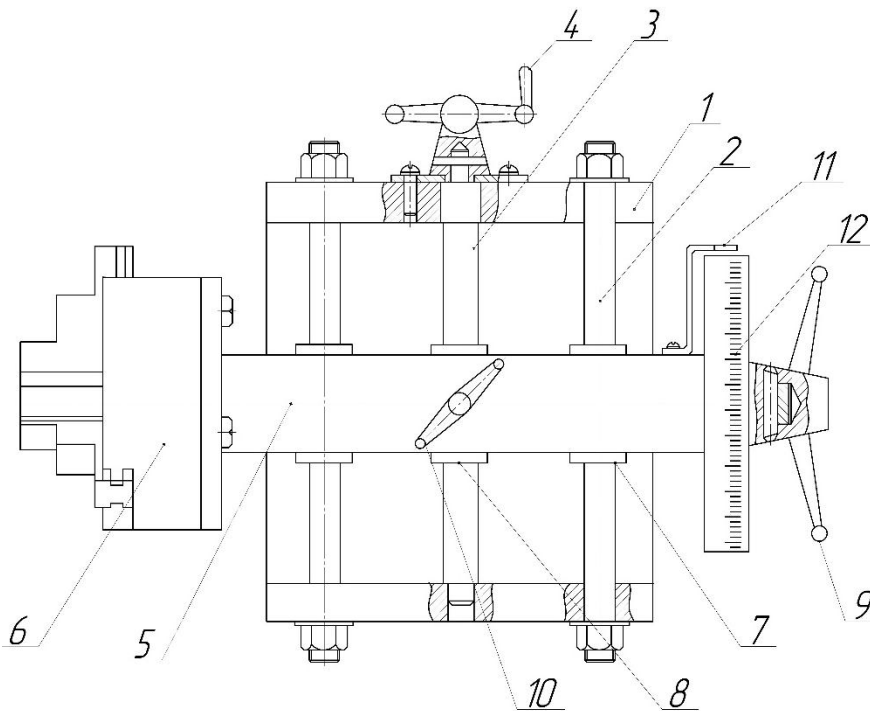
Пристосування для фрезерування на токарному верстаті:
